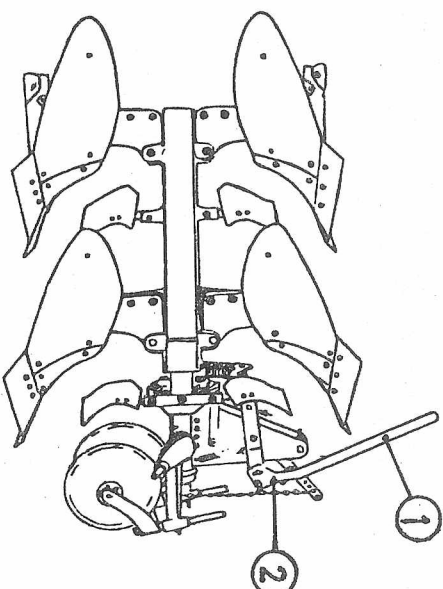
Charrua de dois ferros, reversível (reversão automática e manual) com corpos a 180°, montada
